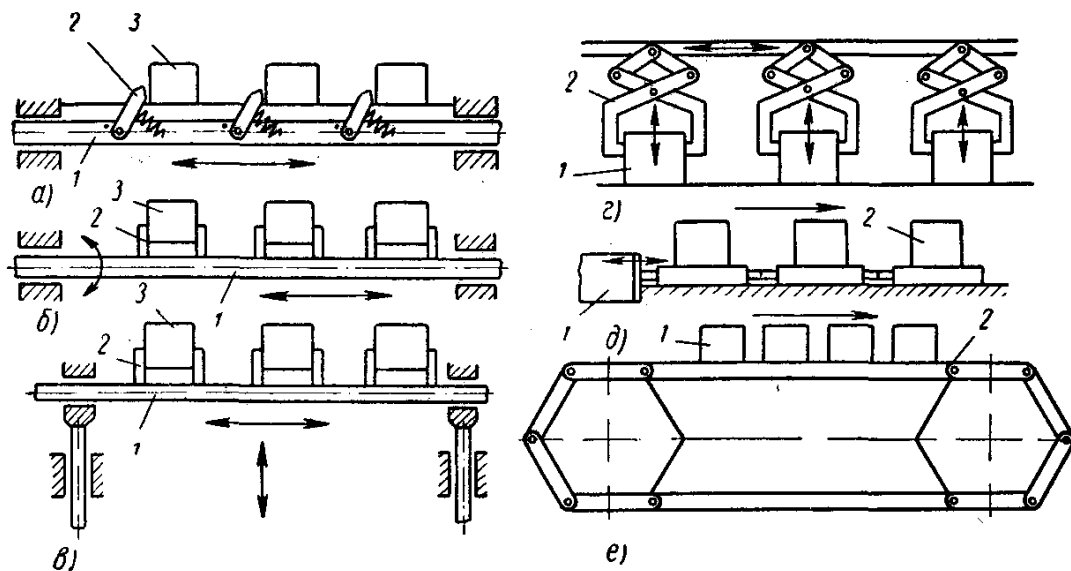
Схеми транспортерів: а- кроковий штанговий транспортер з собачками; б- кроковий штанговий транспортер з флажками; в- грейферний
